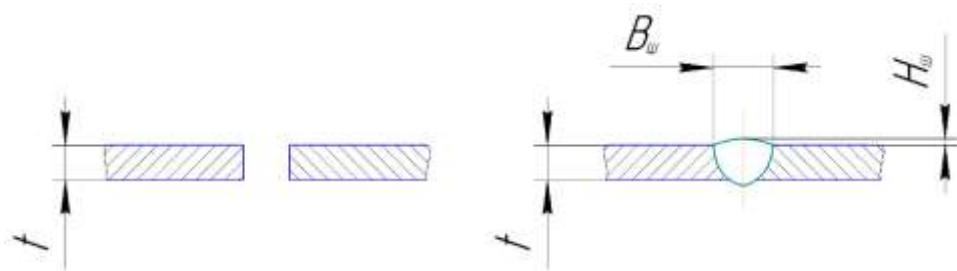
Конструкция сварного соединения и схематичное изображение конфигурации сварного шва с полным проплавлением
